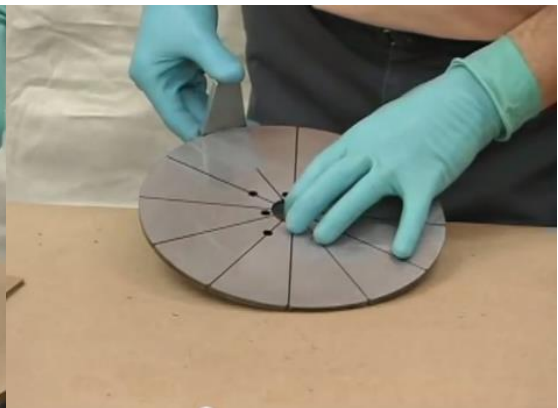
Uložení magnetu na disku axiálního motoru [2]
